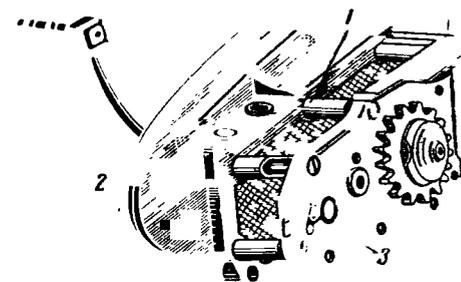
Картер коробки перемены передач мотоциклов «ИЖ», собранный с распорными трубками: 1 — распорная трубка; 2 — крышка картера; 3 — крышка коробки передач.
